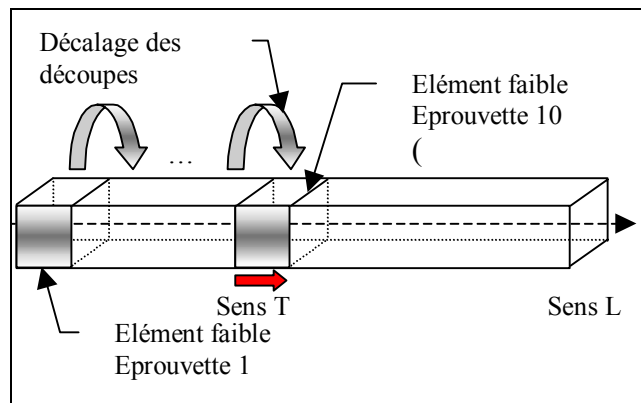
Plan de découpe, inclusion d'un élément faible dans les dix premières éprouvettes.
